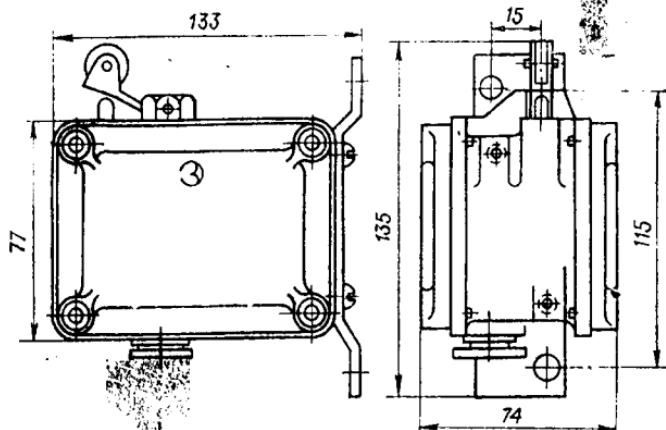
Малогабаритный конечный выключатель типа ВКМ-ВЗГ во взрывозащищенном исполнении ВЗГ (ВЗТ3); корпус из пласти массы.
